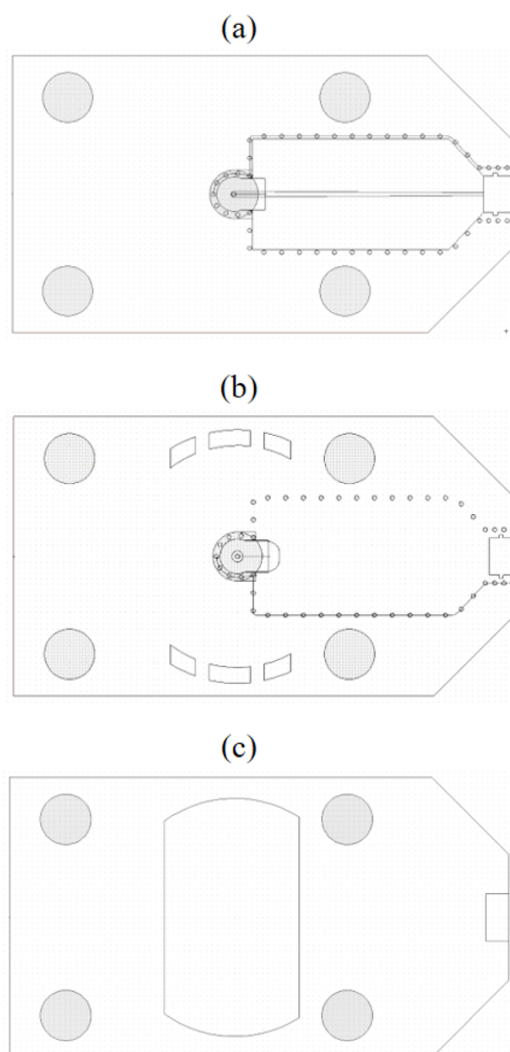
Layouts des différents éléments du PCB HF; (a) face avant et (b) face arrière; (c) couvercle en inox
